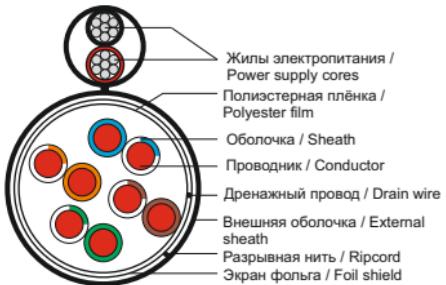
Конструкция кабеля типа F/UTP (с кабелем питания) / Figure 6 – Cable design of F/UTP type (with power supply cable)
